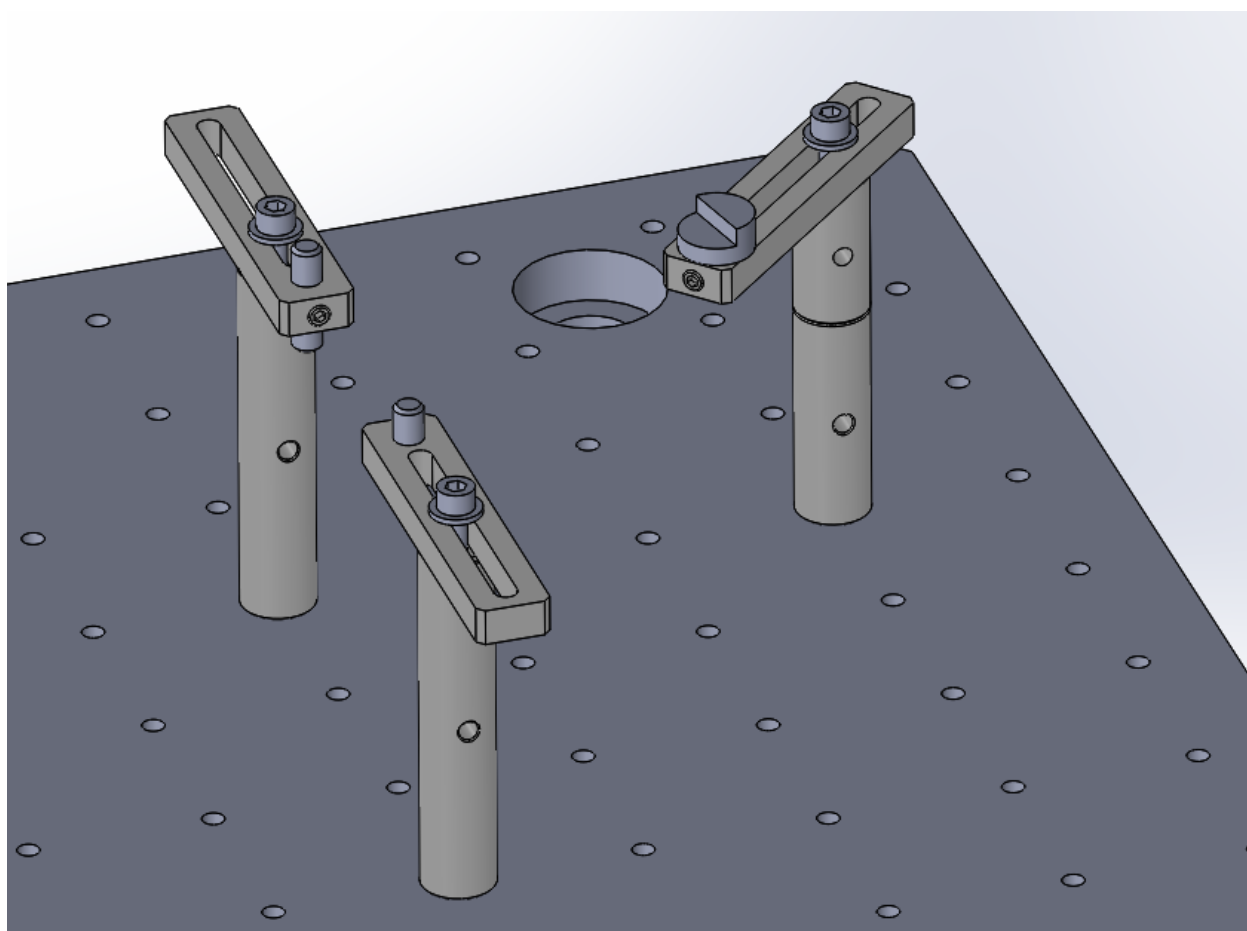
Konstrukce přípravku pro těleso čerpadla
